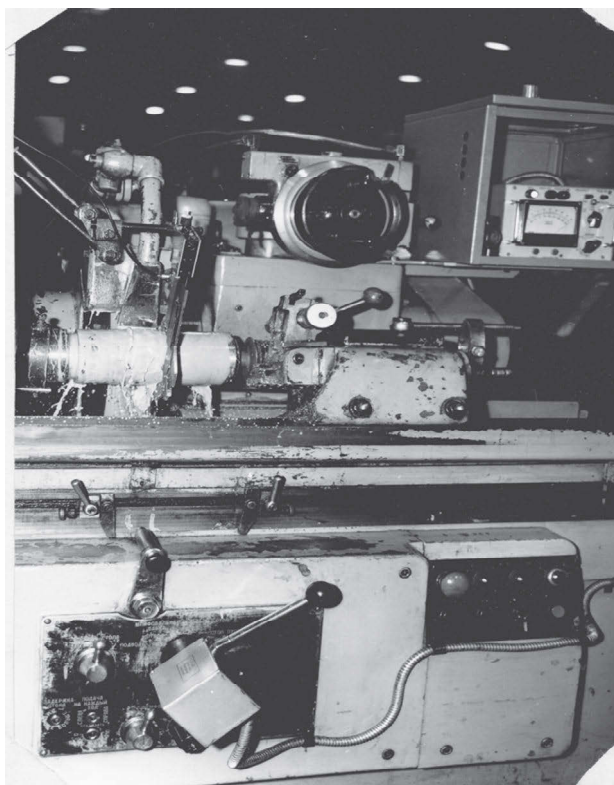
Модернизированный круглошлифовальный станок с прибором активного контроля
